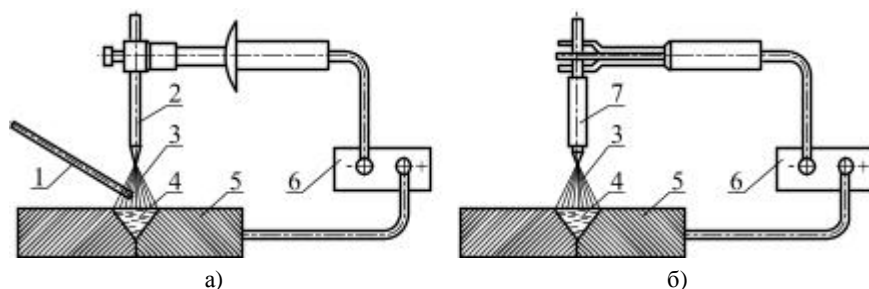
Схема ручного електродугового зварювання без плавлення електрода (а) або з його плавленням (б): 1 – присадний матеріал; 2 – електрод, який не плавиться; 3 – електрична дуга; 4 – ванна з розплавленим металом; 5 – деталь; 6 – джерело живлення; 7 – електрод, який плавиться
